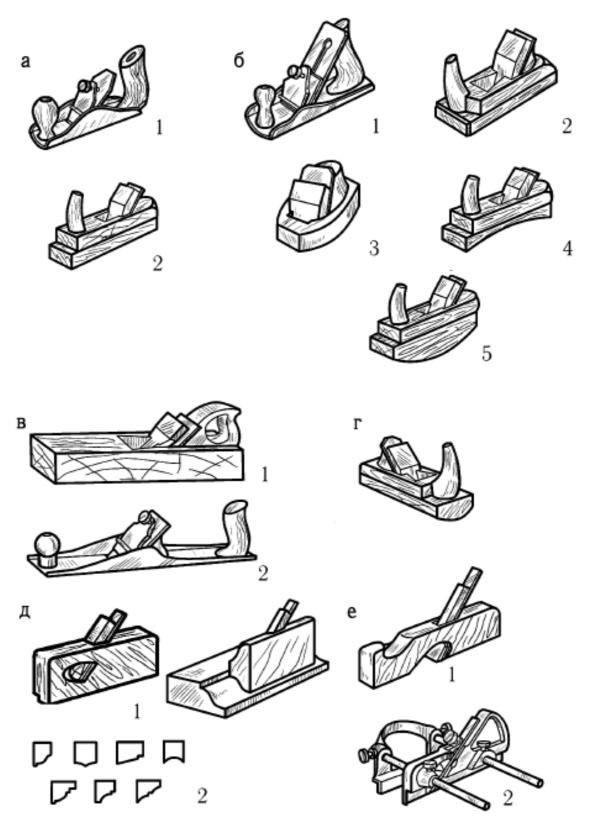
Строгальный инструмент: a — фальцгебель: I — металлический; 2 — деревянный;  $\delta$  — рубанки: I — металлический; 2 — деревянный; 3 — торцевой; 4 — горбач для обработки выпуклых поверхностей;  $\delta$  — горбач для обработки вогнутых поверхностей;  $\delta$  — фуганки:  $\delta$  — деревянный;  $\delta$  — металлический;  $\delta$  — галтель;  $\delta$  — калевка:  $\delta$  — процесс работы;  $\delta$  — профили калевок;  $\delta$  — зензубели:  $\delta$  — деревянный;  $\delta$  — металлический
